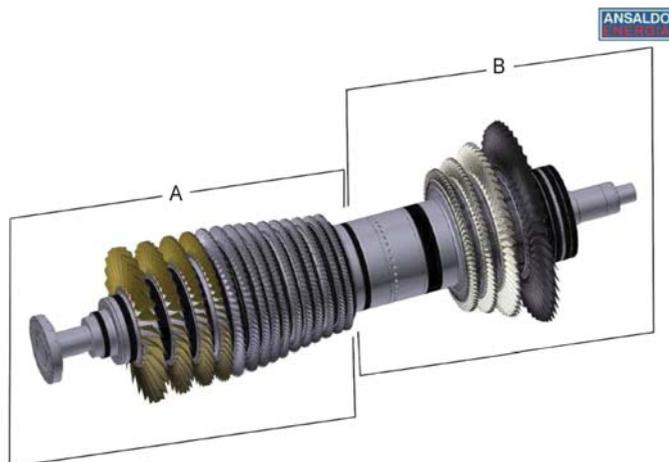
Общий вид ротора в сборе: А) передний полый вал, центральный полый вал, диски компрессора; В) центральный полый вал, задний полый вал, диски турбины, соединительная тяга и гайка крепления соединительной тяги
